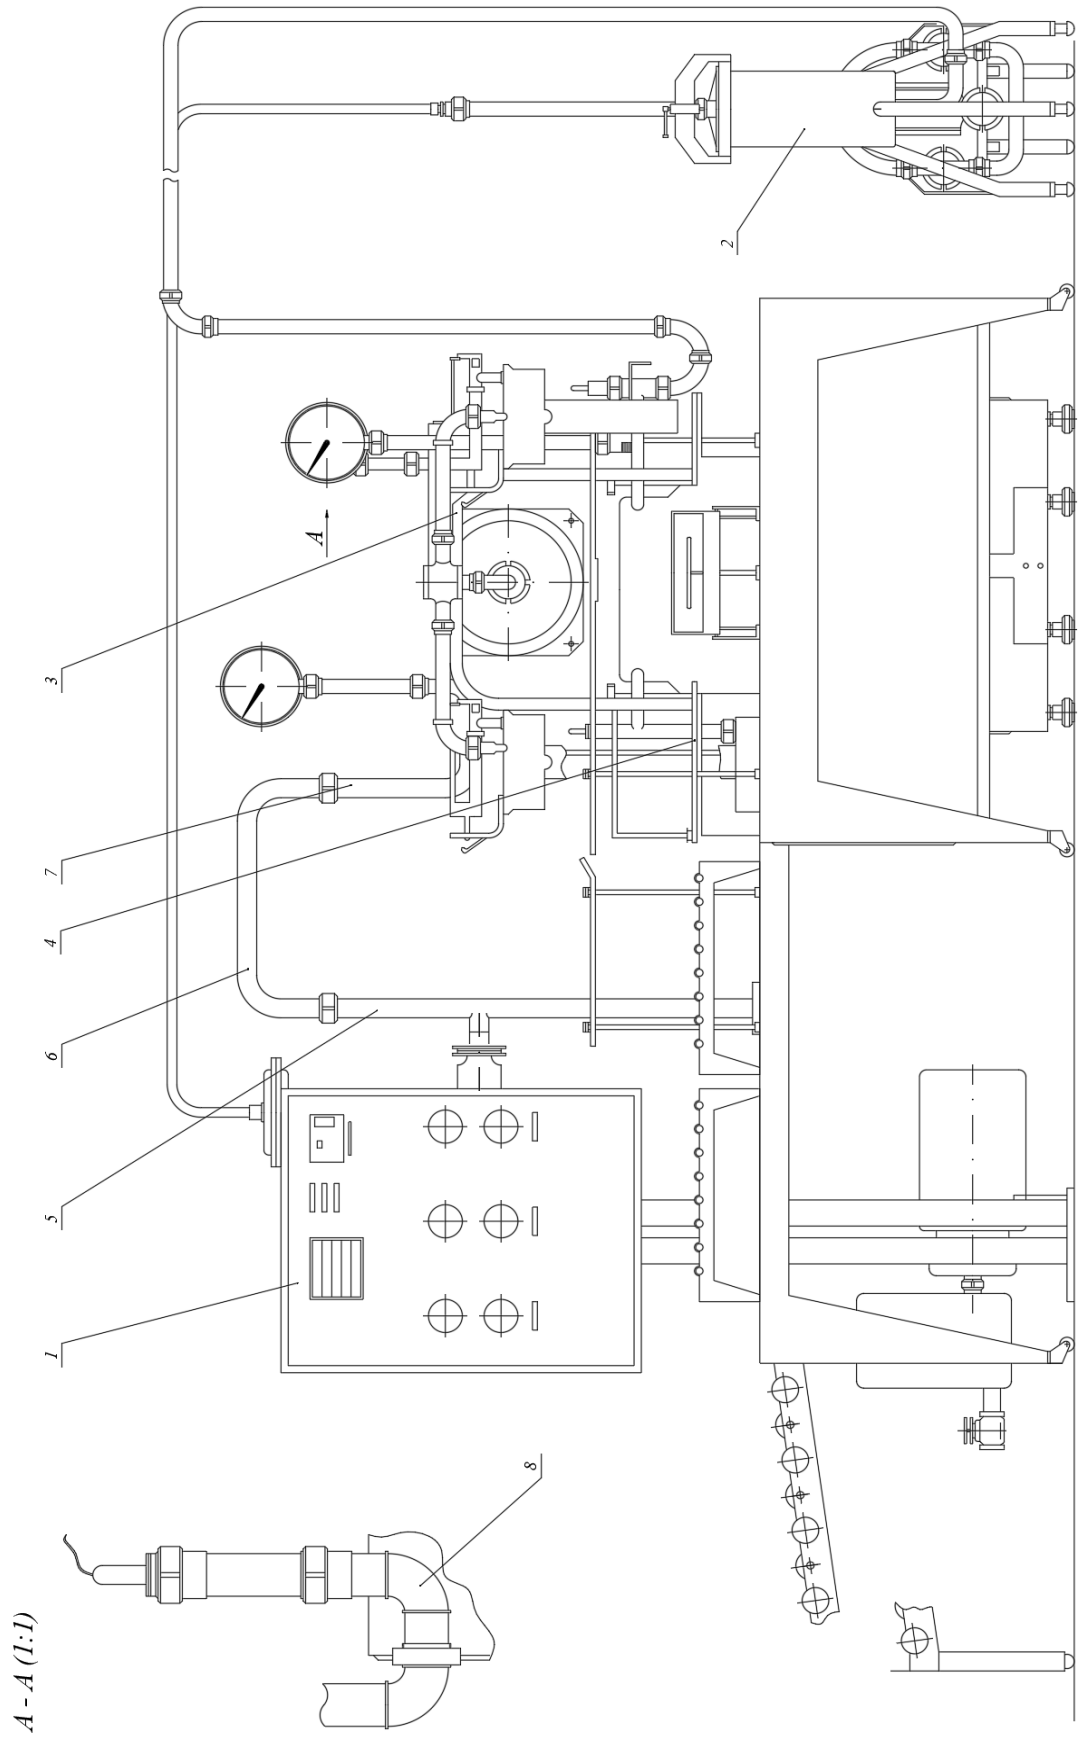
Загальний вигляд комплексу для виготовлення вершкового масла
